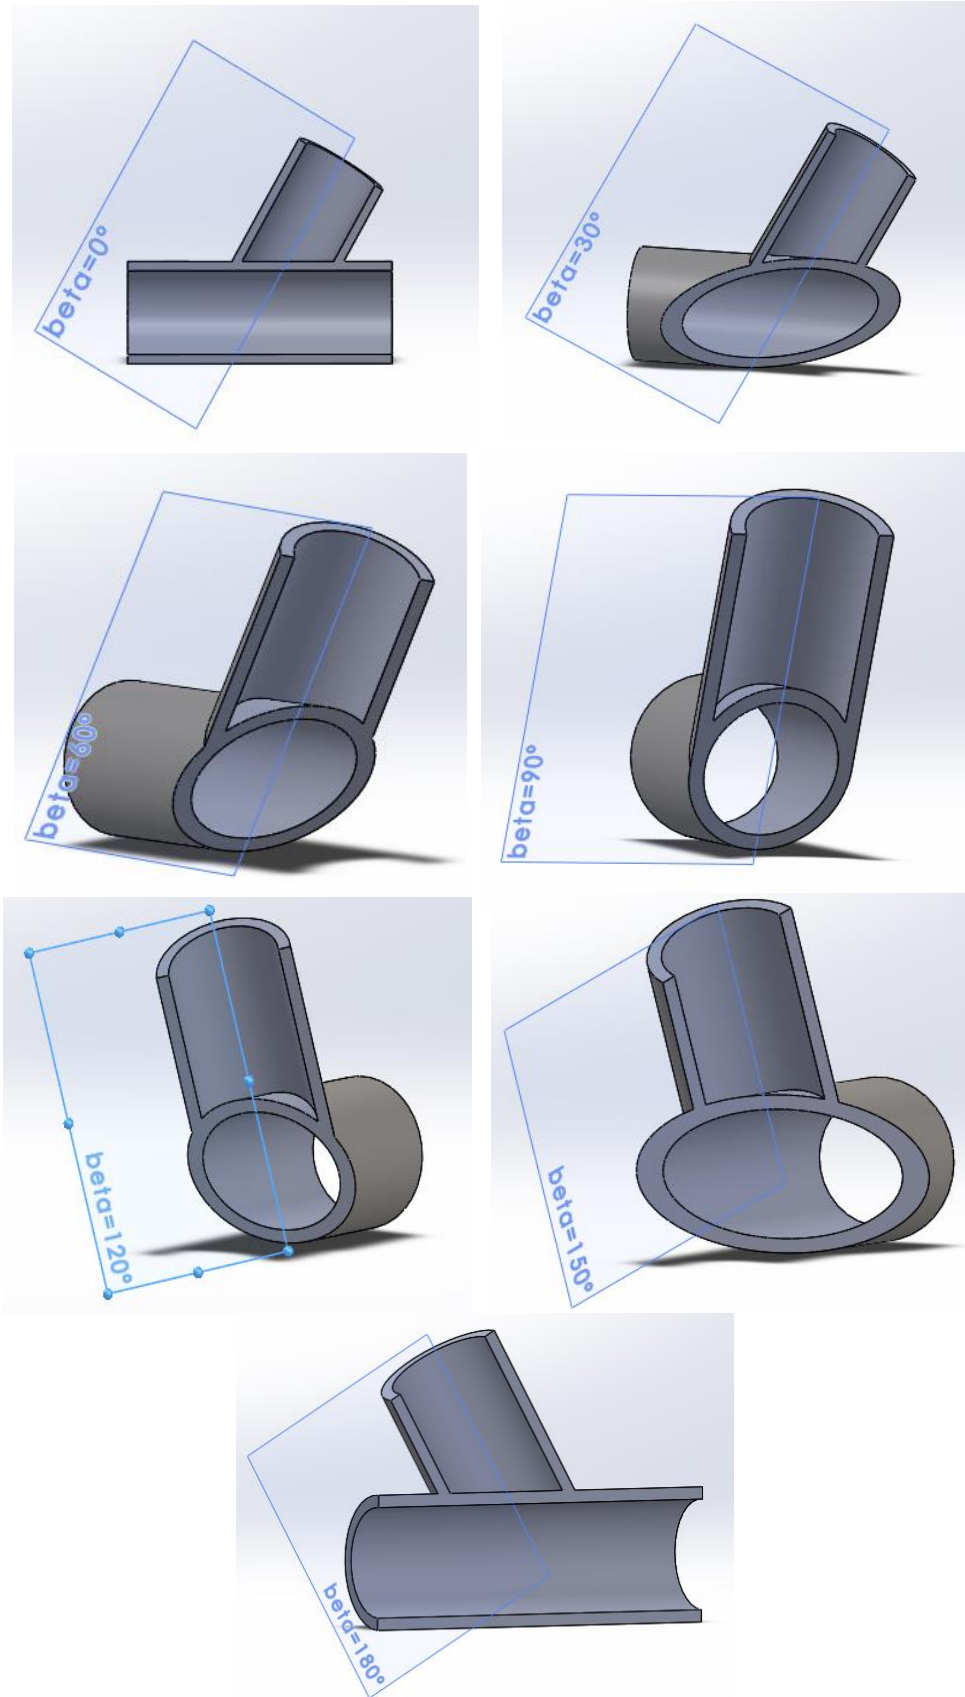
Cortes por diferentes planos de soldadura (Fuente: Propia)
